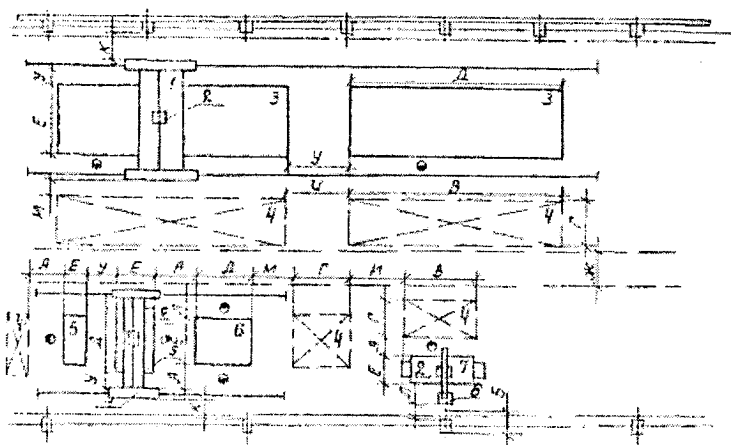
Розміщення установок автоматичного зварювання і різання з поворотними колонами і самохідними порталами :
